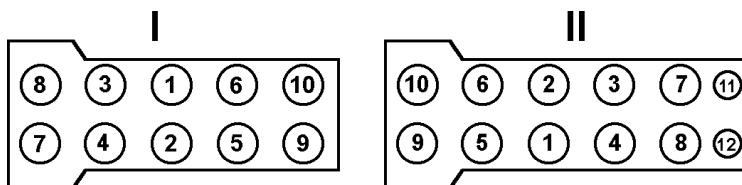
Последовательность затяжки болтов крепления головки блока цилиндров
